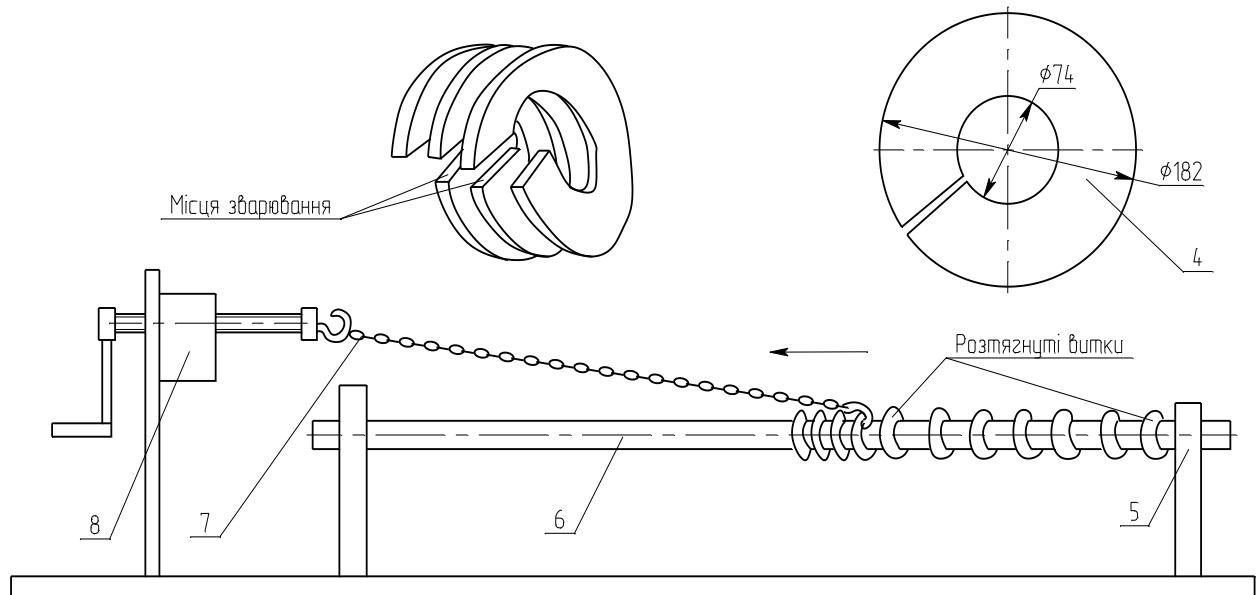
Схема отримання багатовиткової фасонної гвинтової заготовки з гвинтових секційних заготовок.
